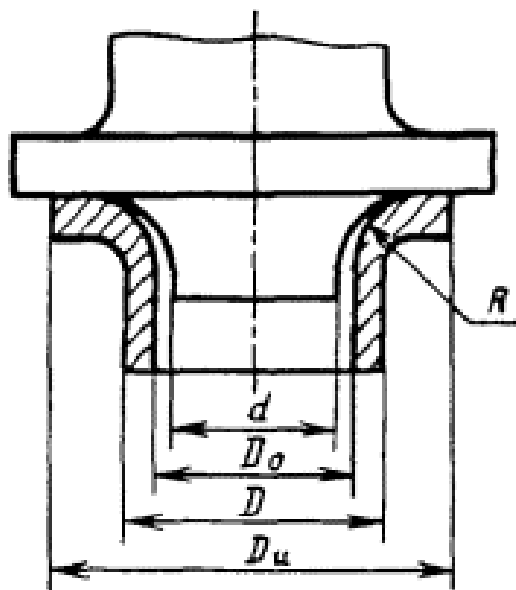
Схема испытания на бортование металлических бесшовных сварных труб: D_u - максимальный диаметр борта; D - наружный диаметр трубы; D_o - внутренний диаметр трубы; d - диаметр оправки; R - радиус борта.
